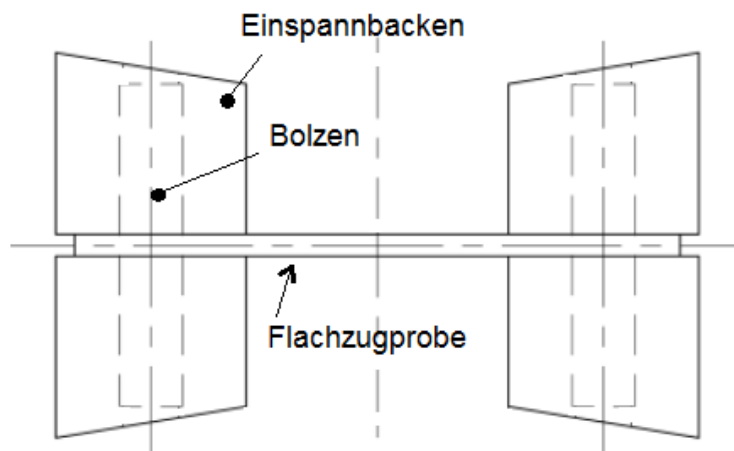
Technische Zeichnung der Flachzugprobe mit den Einspannbacken.
